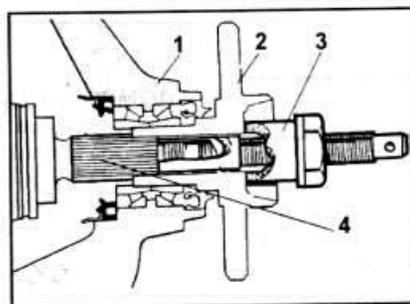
Установка ступицы с помощью приспособления 14-022. 1 - поворотный кулак, 2 - ступица, 3 - приспособление 14-022, 4 - приводной вал.
